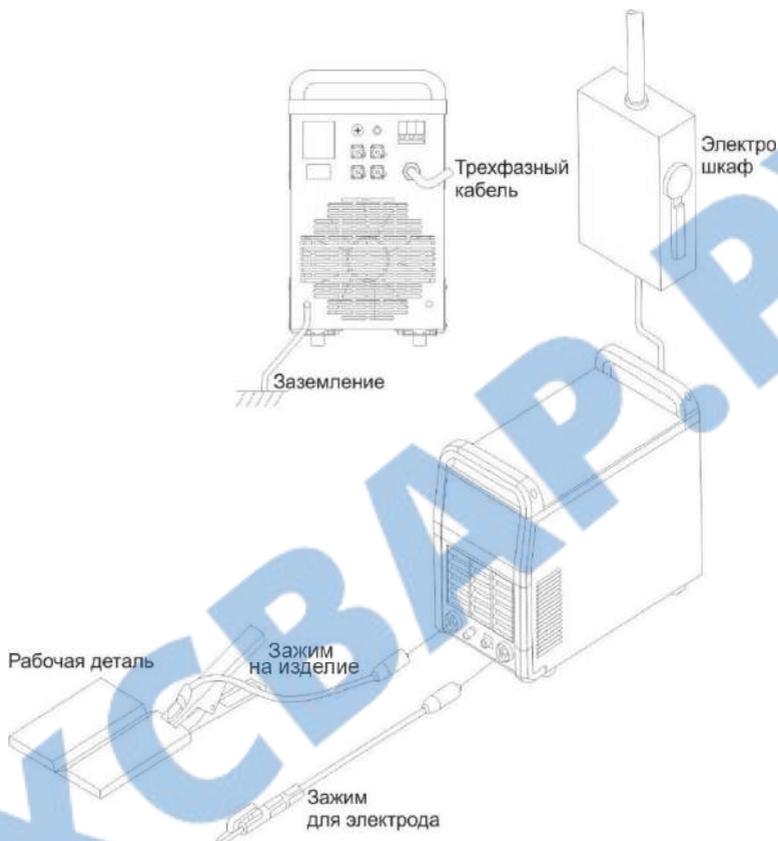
Схема установки аппарата для ручной сварки штучными электродами (стандартная схема для данного сварочного аппарата)
